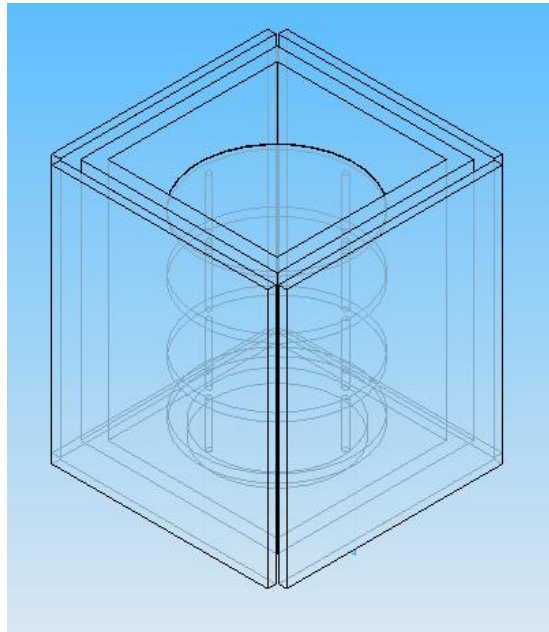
3: Vista Isométrica superior de la parte móvil externa de 6mm
